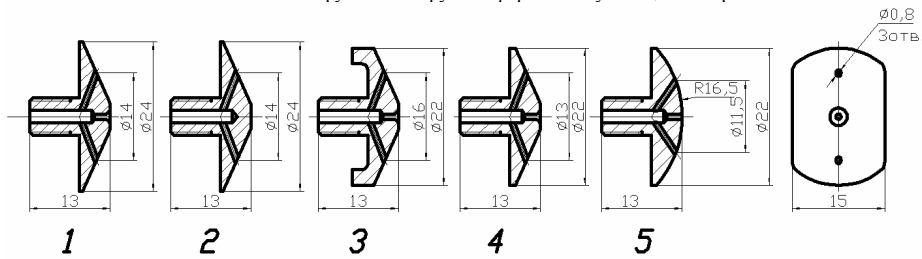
Рабочие инструменты с эллиптической формой излучающей поверхности
